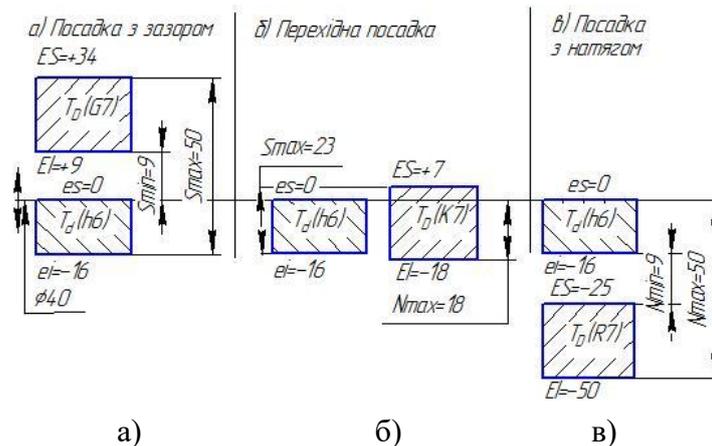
Схема розташування полів допусків посадок
